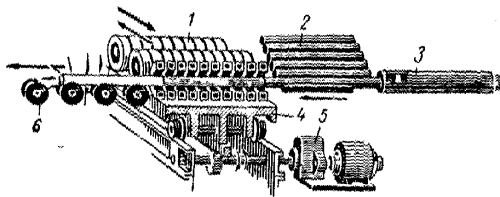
Схема нагревателя с периодическими индукторами, установленными на каретке:
